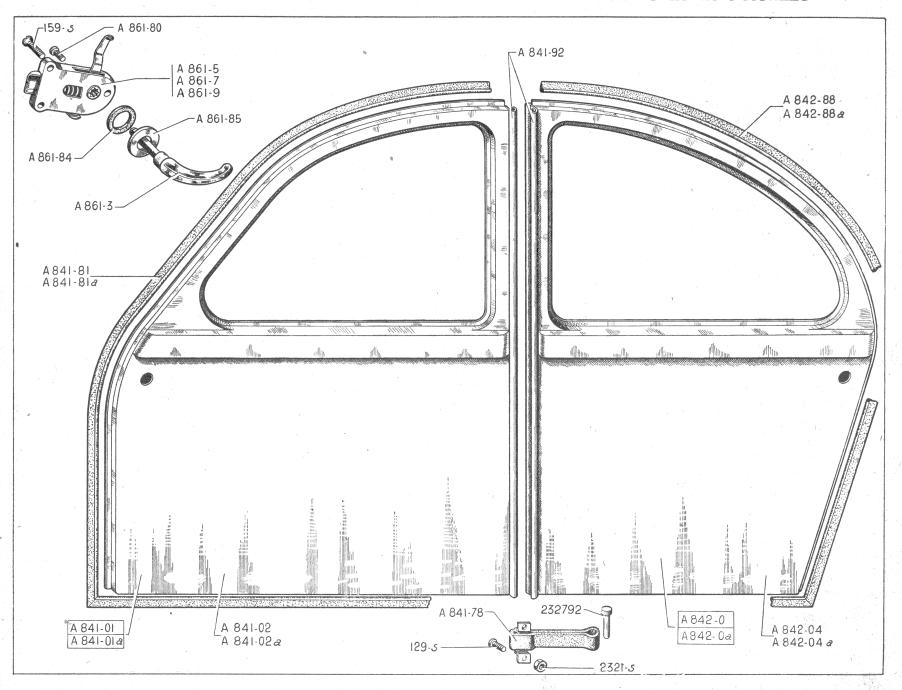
# PLATE-FORME ET ÉLÉMENTS DE CARROSSERIE — 65
